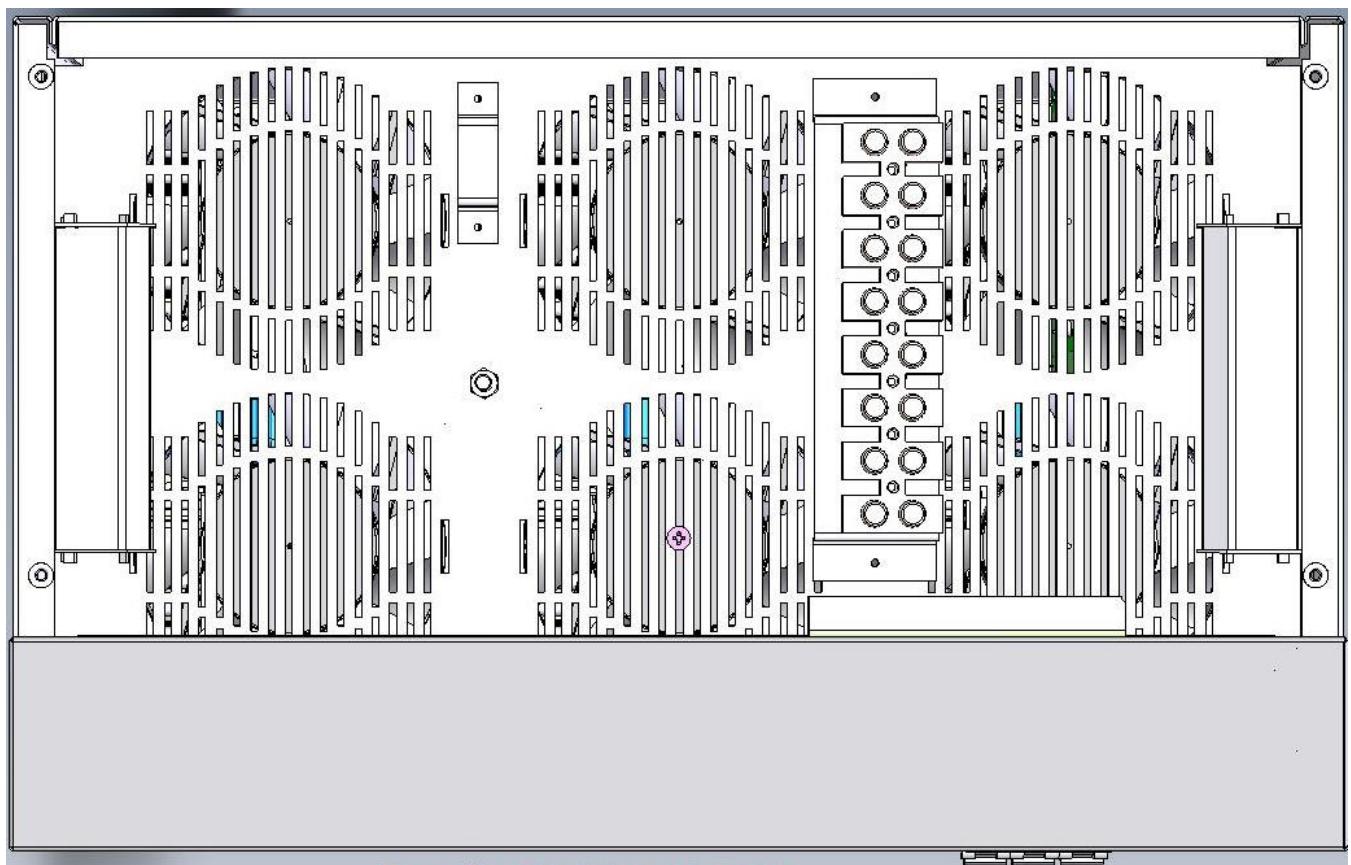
Зовнішній вигляд верхньої частини стабілізатора
